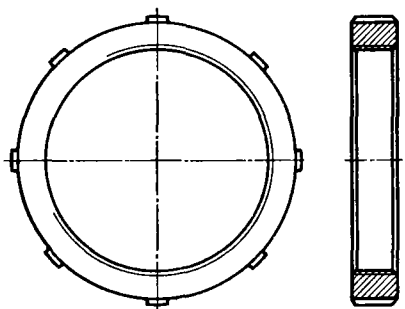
Кольцевая гайка с радиальными зубцами под ключ
